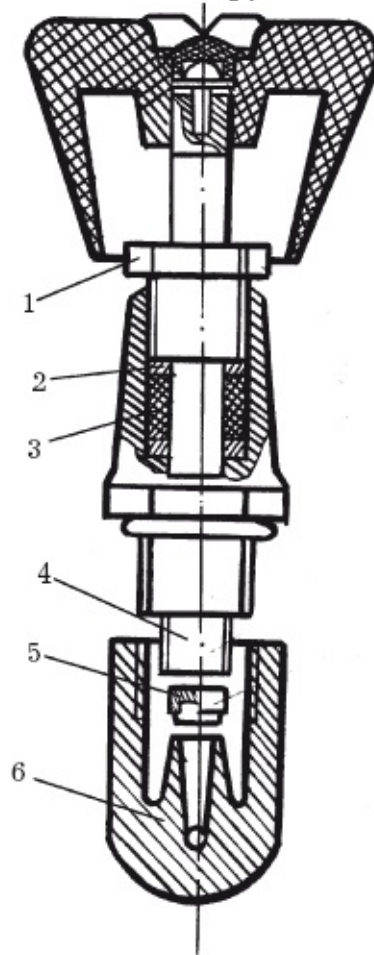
Головка крана: 1 – втулка; 2 – шток; 3 – набивка сальника; 4 – резьба штока; 5 – клапан с прокладкой; 6 – седло клапана
